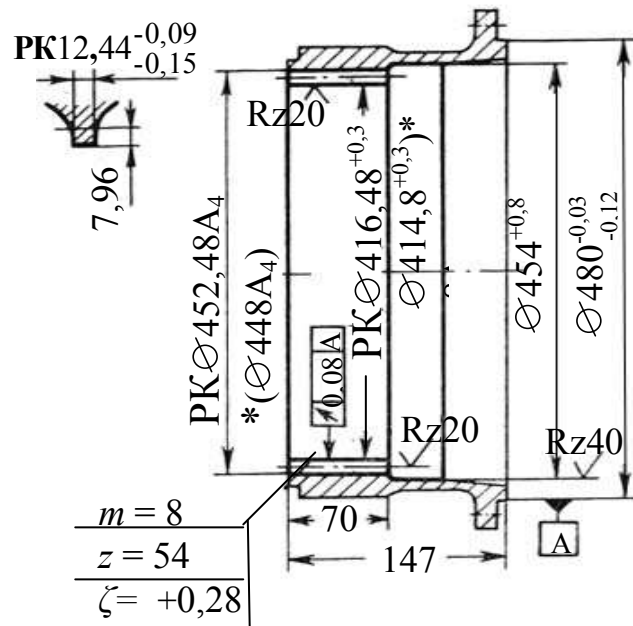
Ремонтный чертеж восстановления венца обоймы зубчатой муфты методом ремонтного корригирования:
